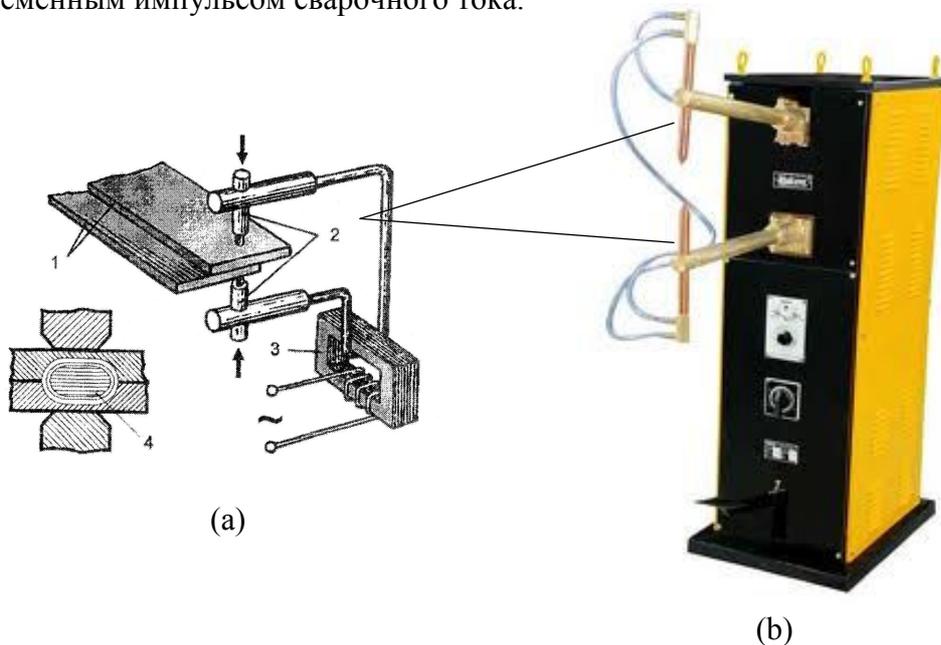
Схема (а) и машина (b) точечной контактной сварки.
